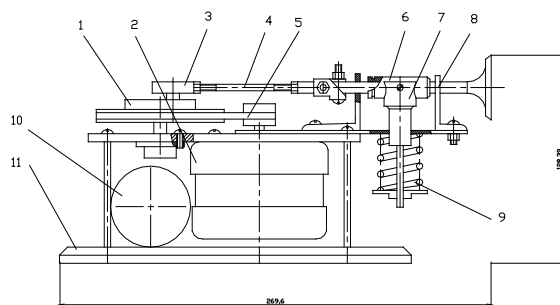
Установка для випробувань на зношування клапанів ДВЗ
